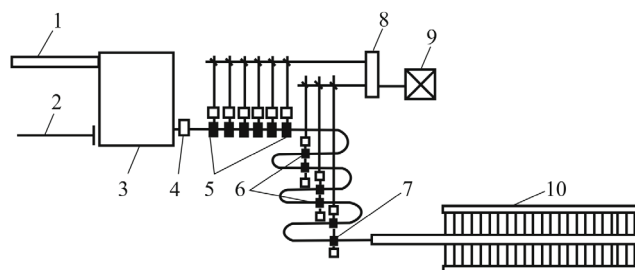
Схема расположения основного оборудования полунепрерывного мелкосортно-проволочного стана [1]: 1 – загрузочный рольганг; 2 – выталкиватель заготовок; 3 – нагревательная печь; 4 – вытаскиватель заготовок; 5 – черновая группа клетей; 6 – промежуточная группа клетей; 7 – чистовая группа клетей; 8 – редуктор; 9 – электродвигатель; 10 – холодильник
